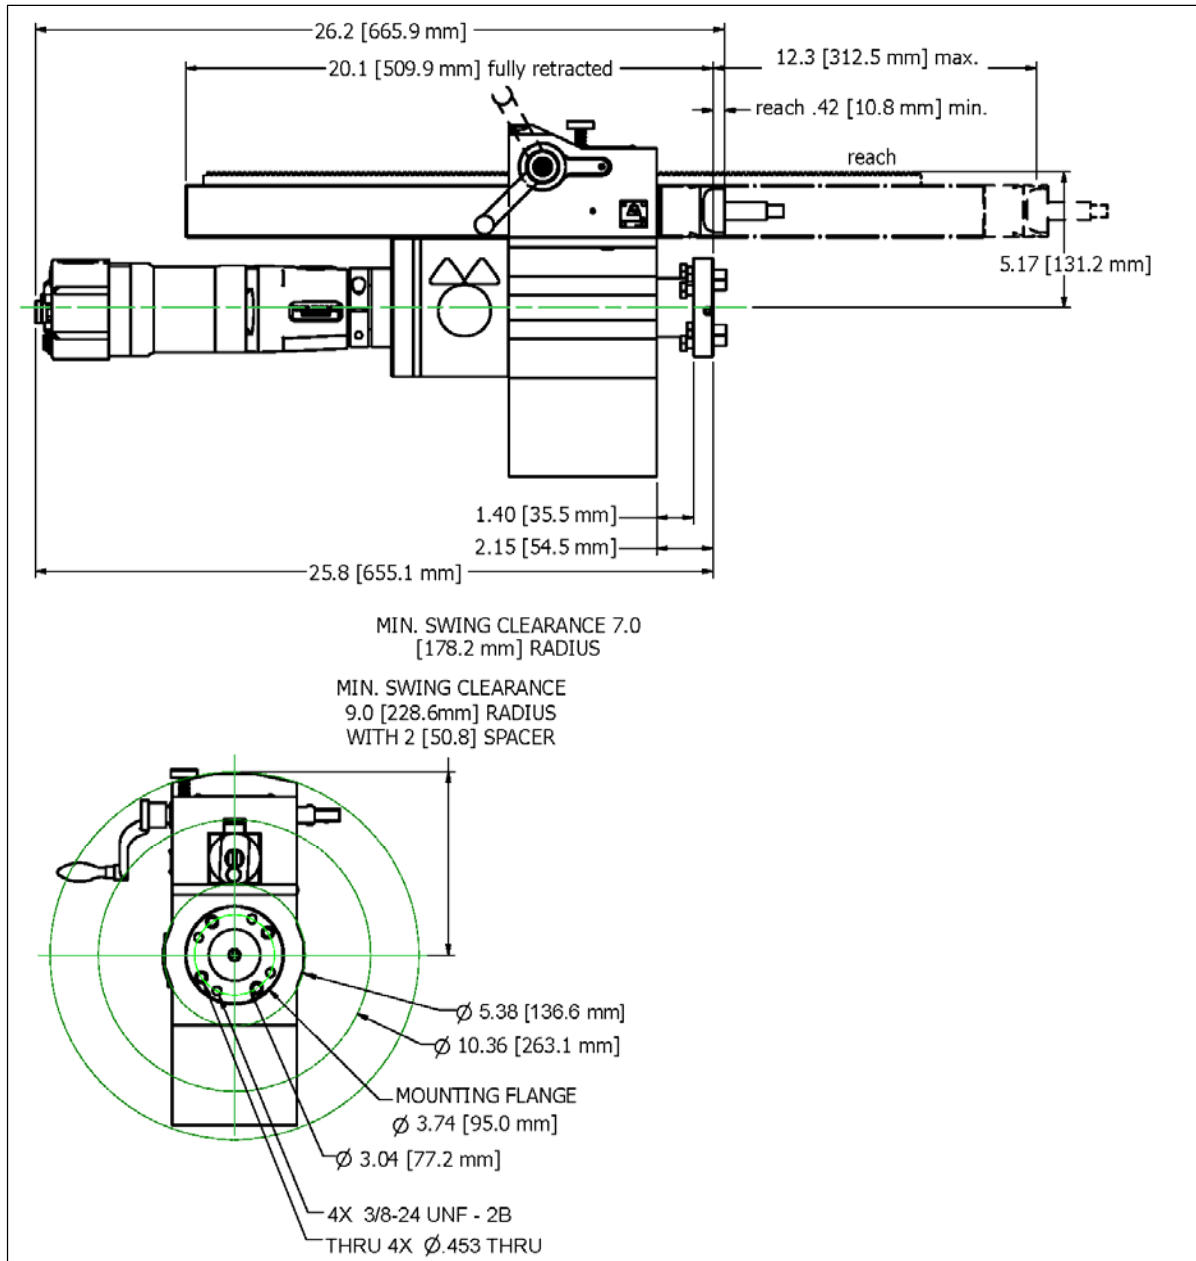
DIMENSIONS DE DEGAGEMENT DU TOUR PORTATIF ELECTRIQUE (POUCES/MM)
